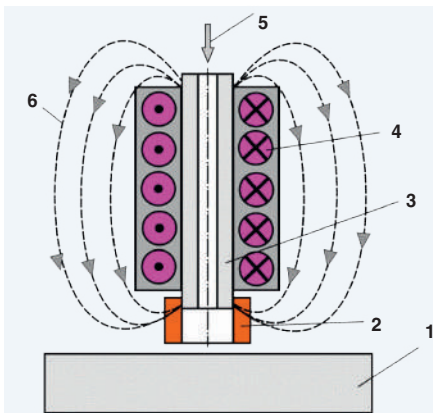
Схема ЭДФ с наложением вращающегося магнитного поля: 1 — заготовка; 2 — медный электрод-инструмент; 3 — сердечник; 4 — катушки возбуждения; 5 — подача диэлектрика под давлением; 6 — линии магнитного поля
